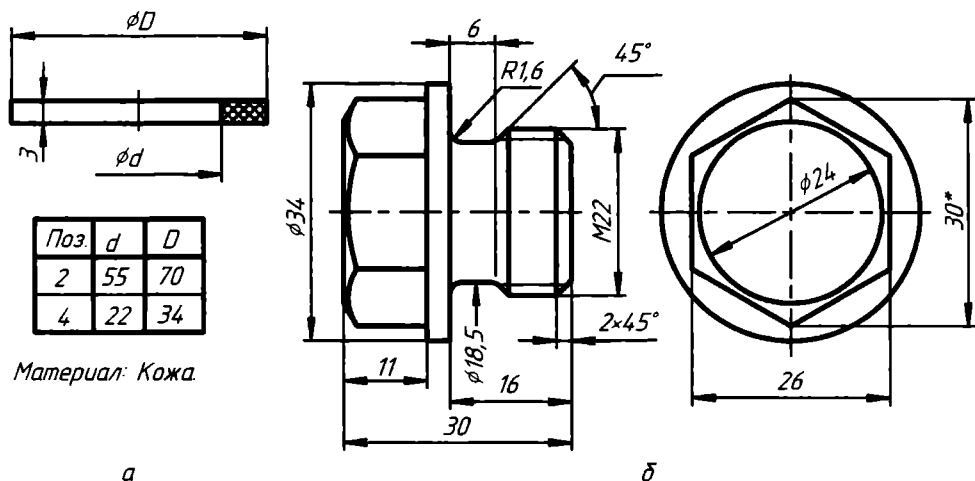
Чертежи: а — прокладок; б — пробки
